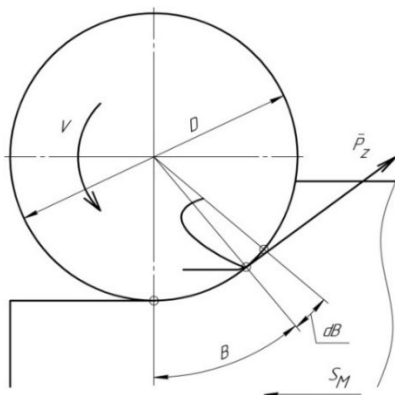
Схема для определения главной (окружной) составляющей силы резания при фрезеровании цилиндрической фрезой
